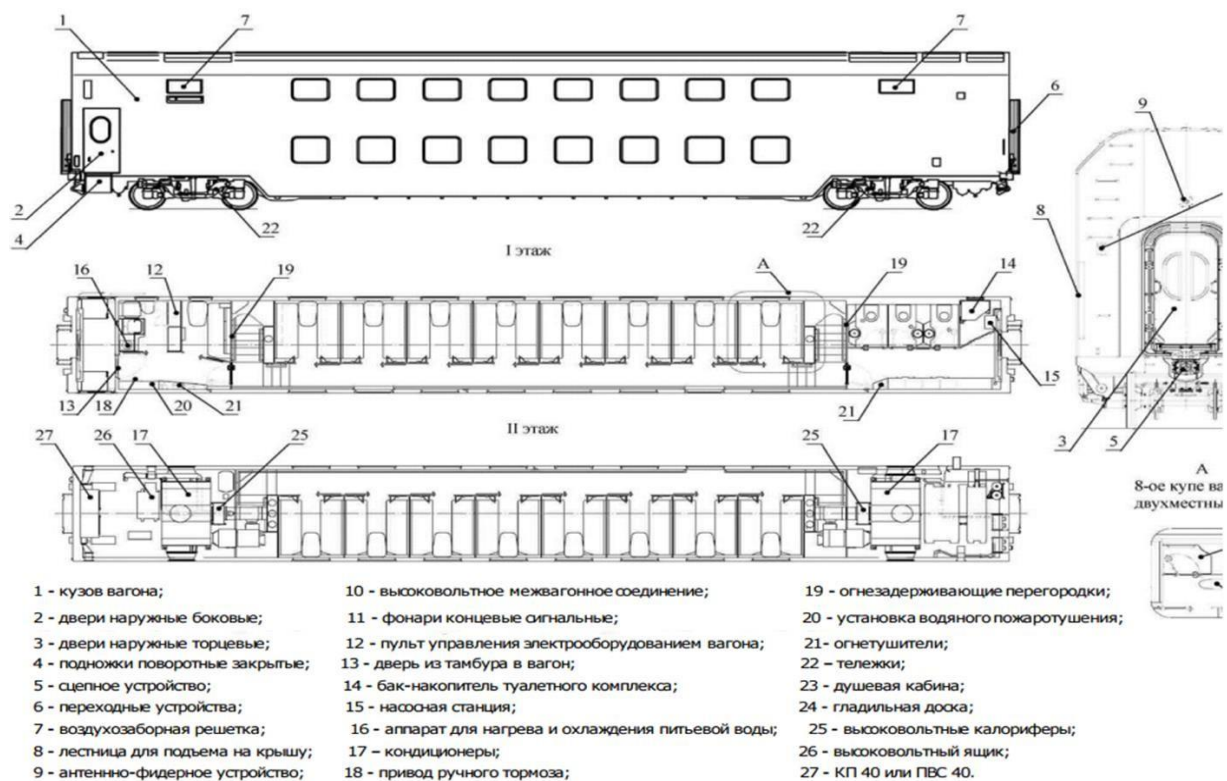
Двоповерховий пасажирський вагон моделі 61-4465. Планування першого і другого поверху
